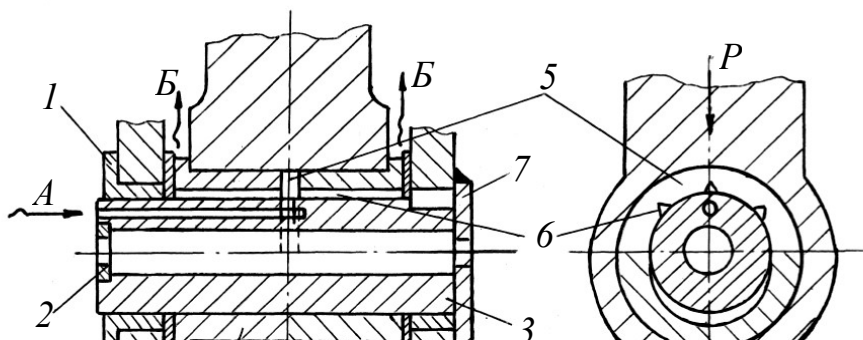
Конструктивная схема и смазка шарниров рабочего оборудования:
